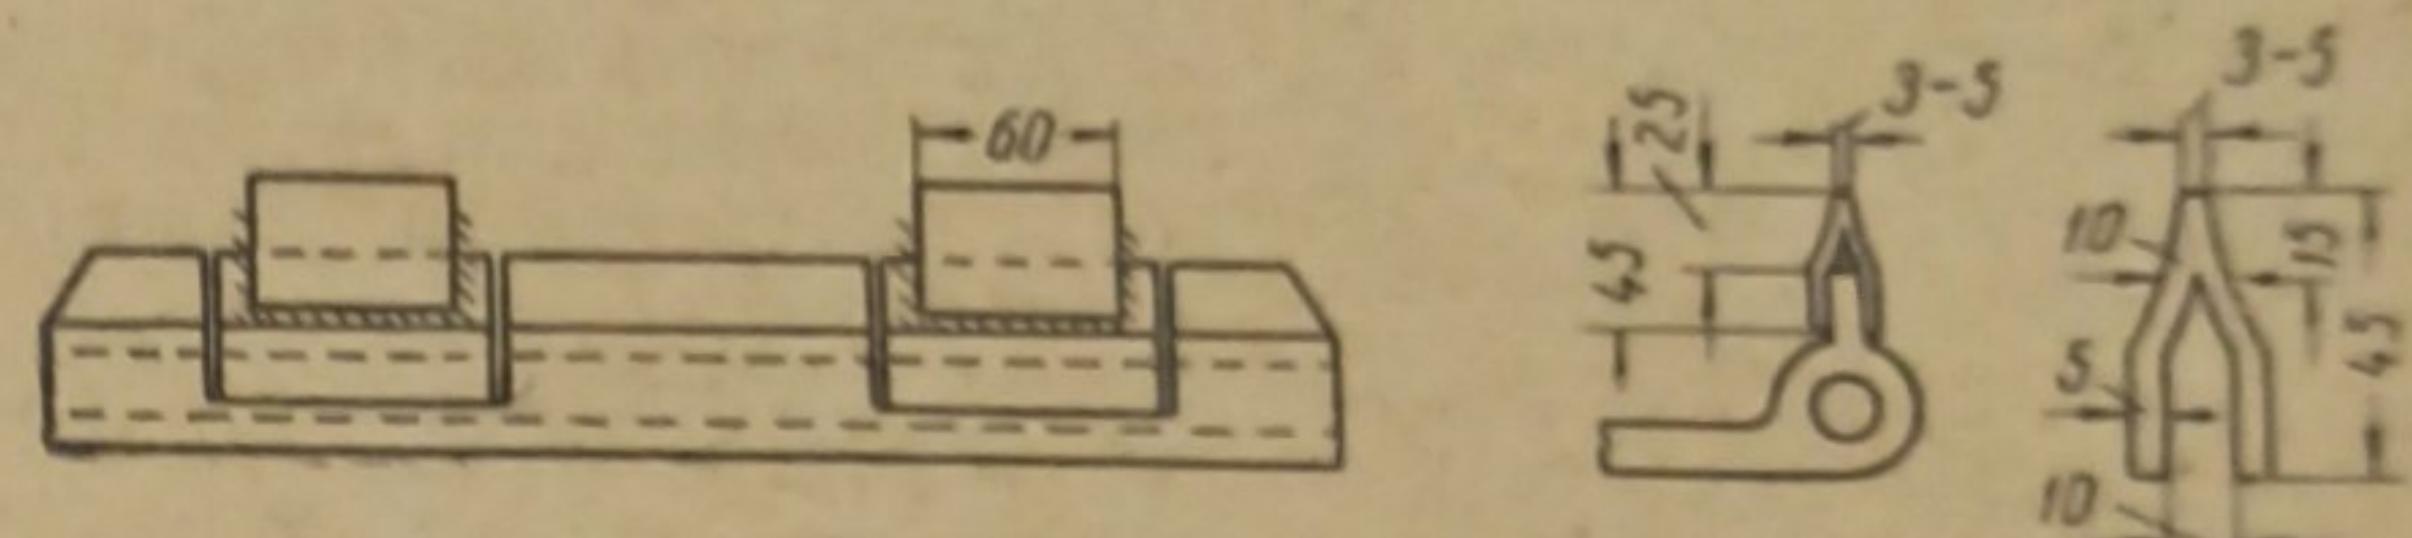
Общий вид башмака гусеницы трактора ХТЗ-НАТИ с наваренными шипами. Справа — вид шипа до наварки
